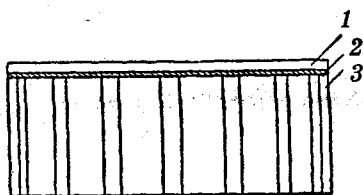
Напайка пластины на торцевую поверхность шестерни подкачивающей помпы:
